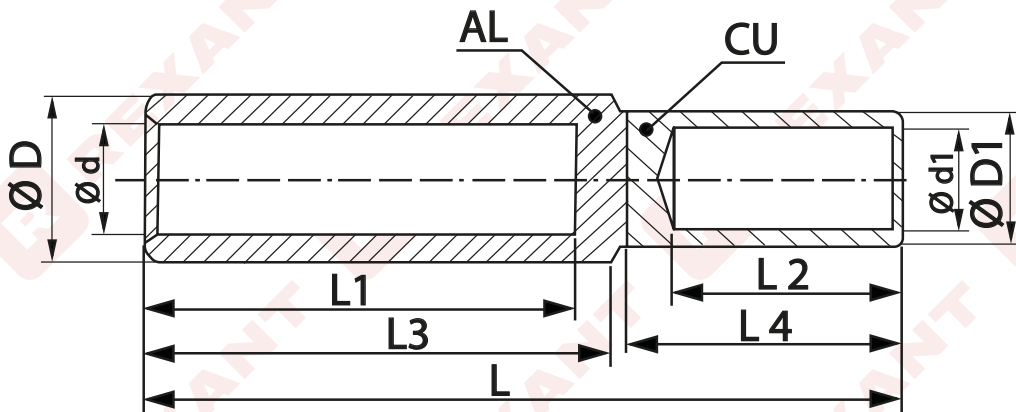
Гильзы медно-алюминиевые, внешний вид и габаритные размеры
